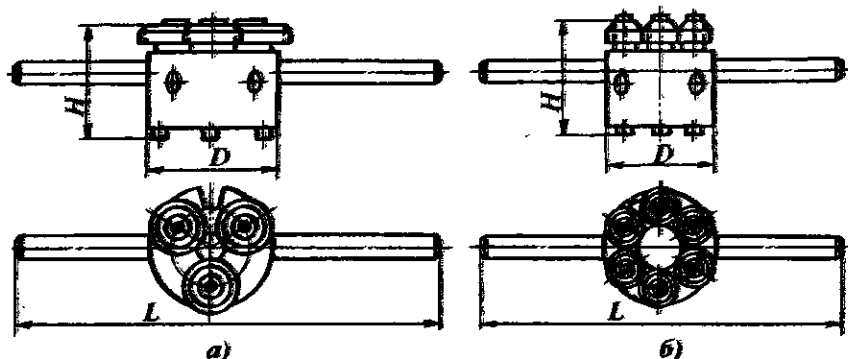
Резьбокатные планки типа: а — НП, б — ННТ
